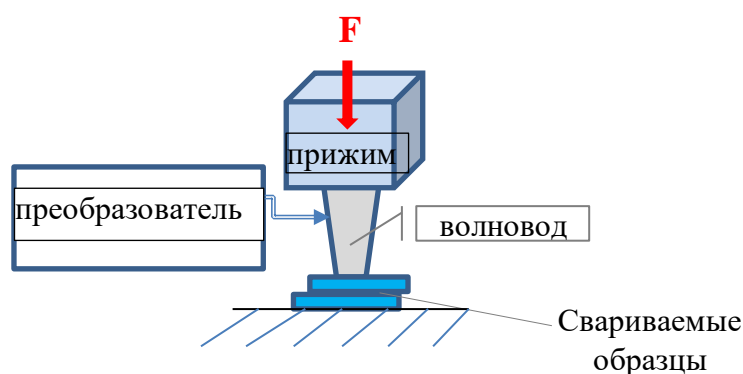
Схема ультразвуковой сварочной установки
